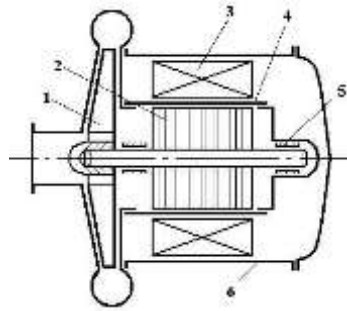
Схема герметичного насоса: 1 – робоче колесо; 2 – ротор електродвигуна; 3 – статор електродвигуна; 4 – екран; 5 – підшипники; 6 – корпус
